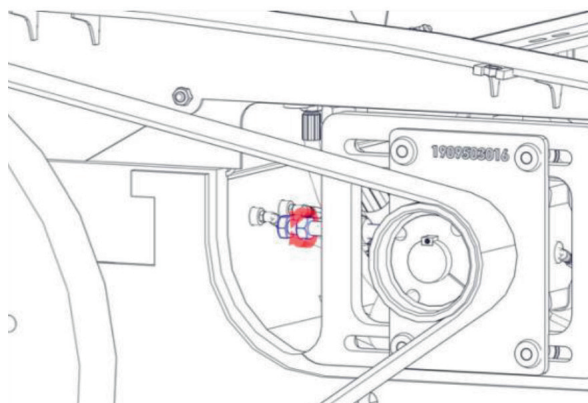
Замена ремня: ослабить подшипник промежуточного вала. Ослабить болты М16 со стороны подшипника промежуточного вала.
